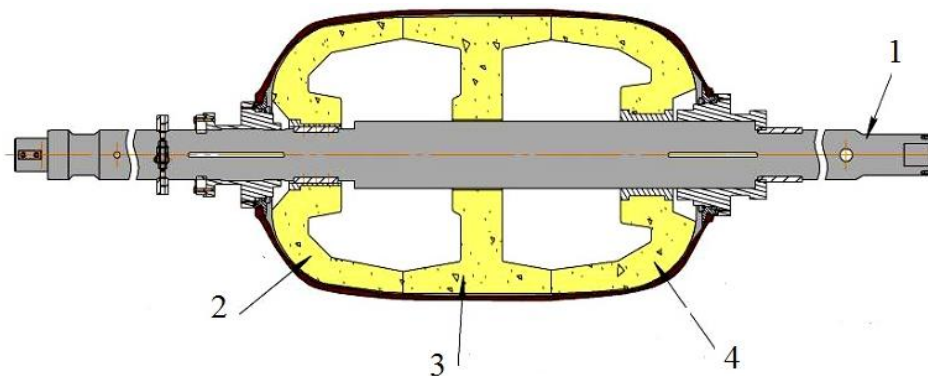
Конструктивная схема разрушаемой оправки:
